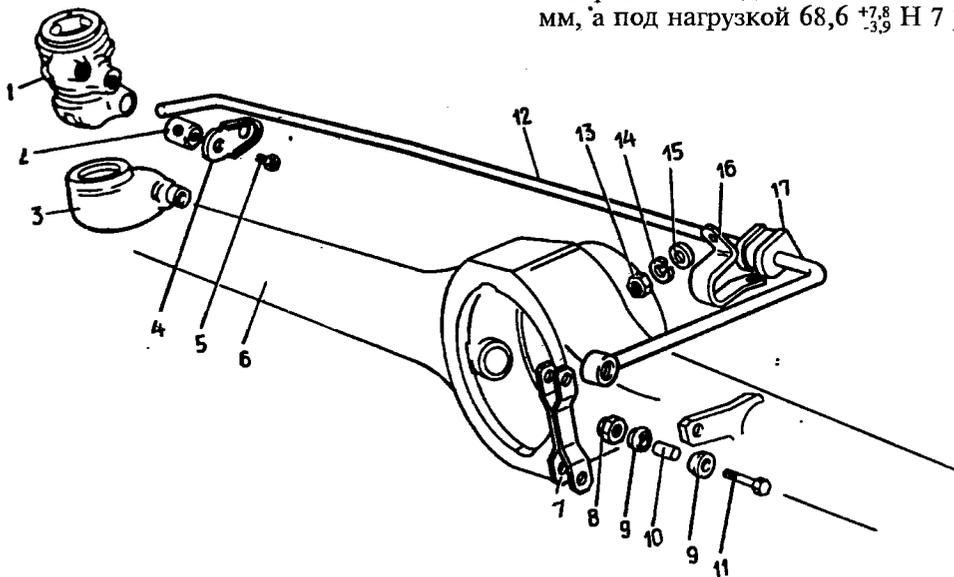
Детали привода регулятора давления: 1 - регулятор давления; 2 - ось рычага привода регулятора давления; 3 - грязезащитный колпачок; 4 - стопорная пластина; 5 - болт с пружинной шайбой; 6 - задний мост; 7 - тяга соединения рычага привода регулятора давления с кронштейном заднего моста; 8 - гайка болта; 9 - пластмассовая втулка; 10 - распорная втулка; 11 - болт крепления тяги; 12 - рычаг привода регулятора давления; 13 - гайка для крепления скобы к кузову; 14 - пружинная шайба; 15 - плоская шайба; 16 - скоба крепления рычага привода регулятора давления; 17 - резиновая втулка
